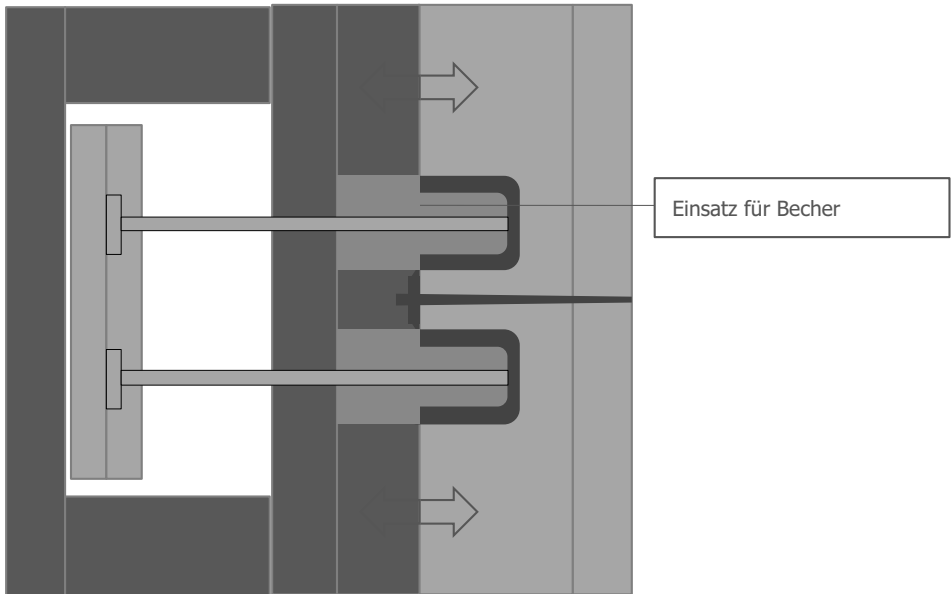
Becherwerkzeug mit Punktanguss – geschlossen
